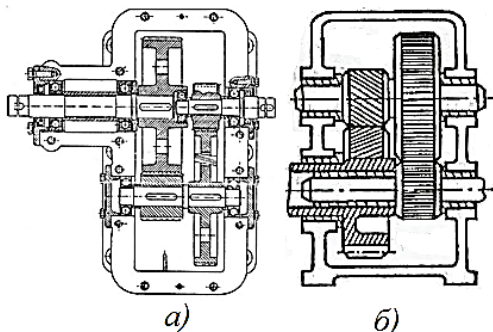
Совершенствование конструктивной схемы редуктора
